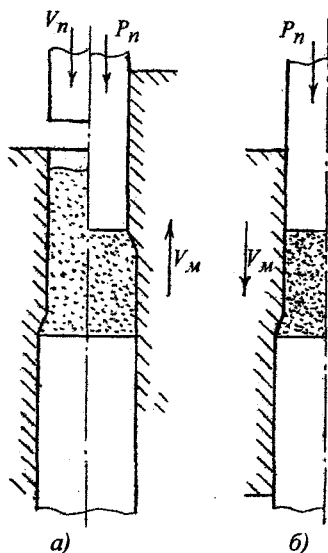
Схема формования порошковой заготовки осевым сжатием с созданием сдвигов слоев материала
